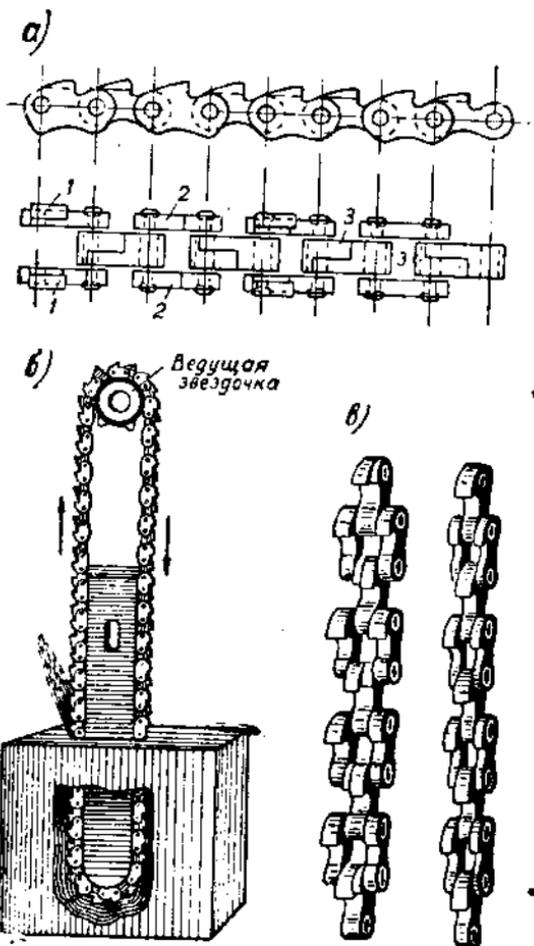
Долбежная цепь: а—зубья звеньев 1—зуб режущего звена, 2—защищающие двойные зубья, 3—зуб выбирающего звена; б—цепь; в работе; в—общий вид цепей.
